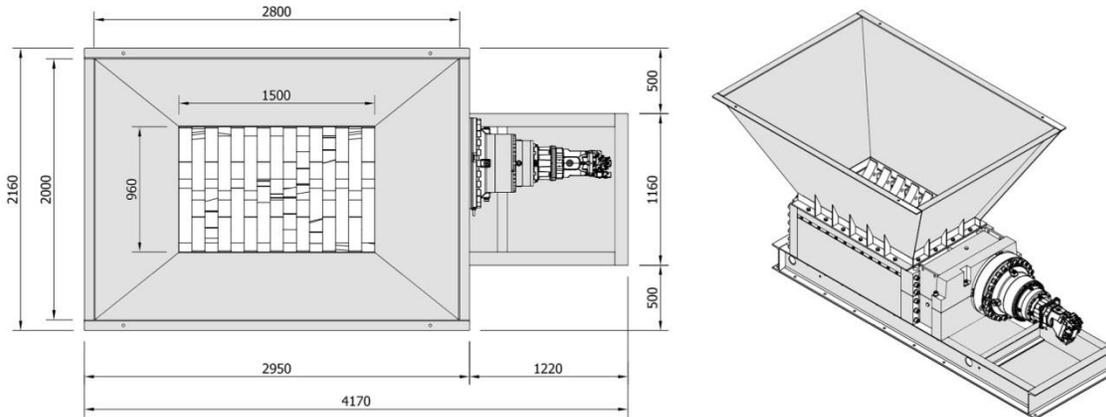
Dimensiones Maquina Trituradora (Coparm)
